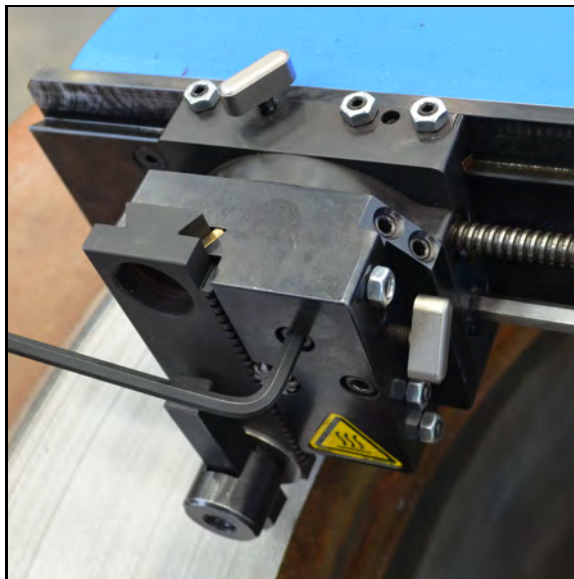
Стопорный винт поворотной головки на передней стороне инструментальной стойки
